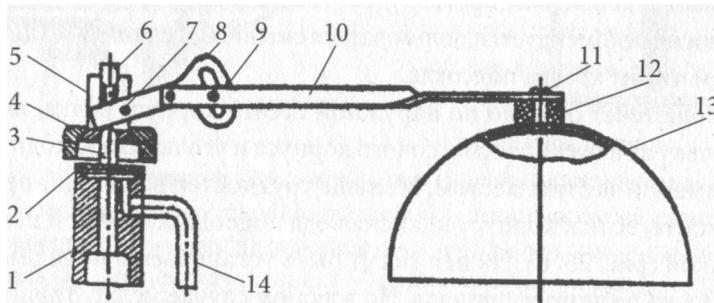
Устройство вертикального поплавкового клапана: 1 — корпус; 2 — резиновая прокладка; 3 — шток; 4 — накидная гайка; 5 — валик; 6 — спецвинт; 7 — шплинт; 8 — рычаг фасонный; 9 — барашек; 10 — рычаг поплавка; 11 — винт; 12 — втулка пластмассовая; 13 — поплавок; 14 — трубка сливная
